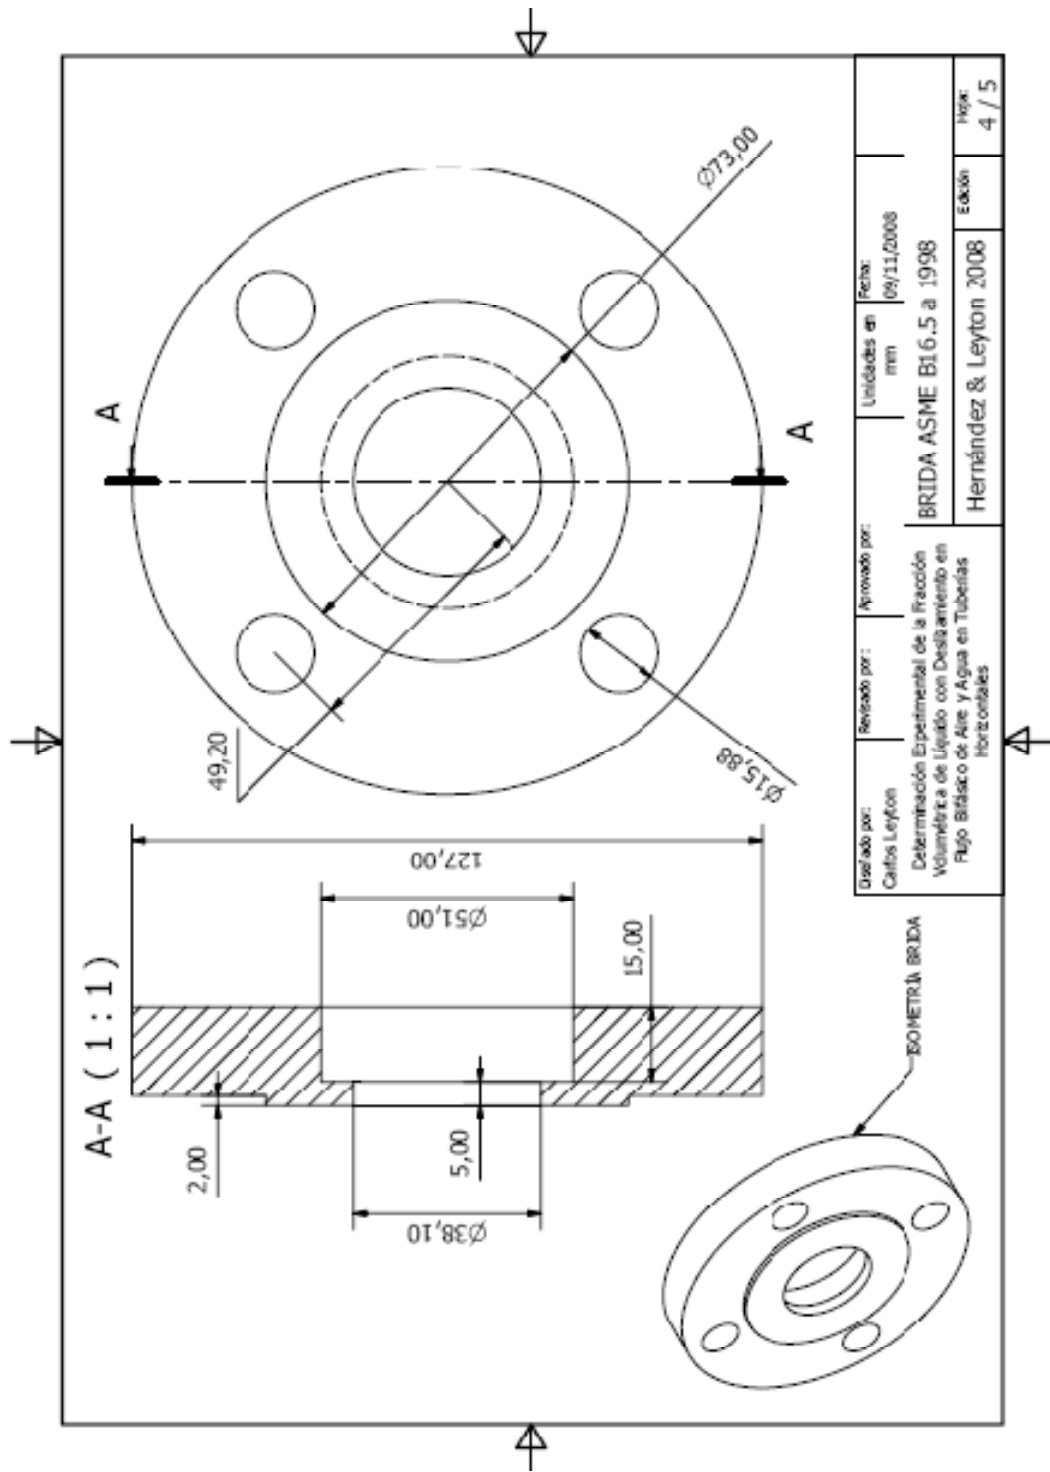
Planos constructivos de la Sección de desvío de flujo (4/5).
